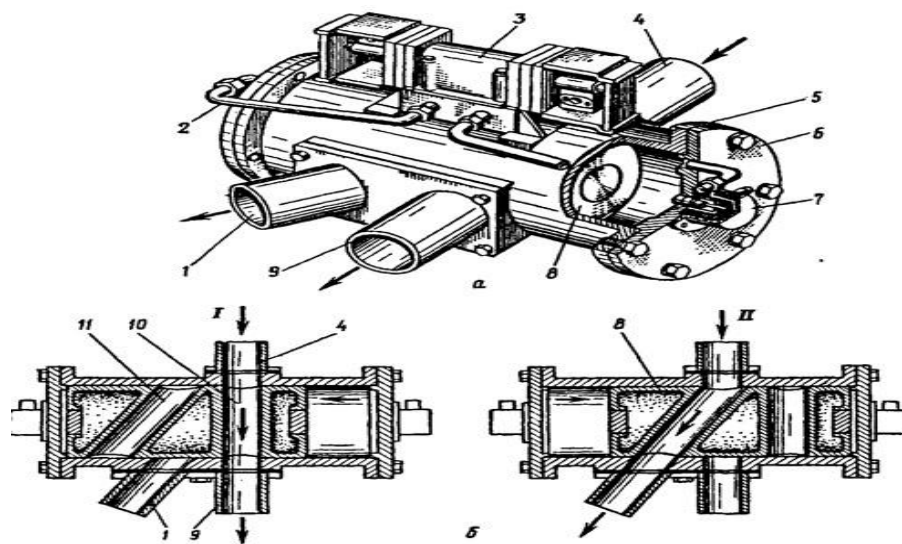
Двухпозиционный переключатель с пневмоприводом: а — общий вид; б — схема работы
